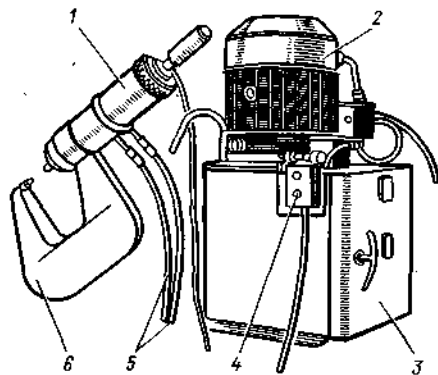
Установка для клепки рам: 1— силовая головка; 2— электродвигатель; 3— корпус; 4— пусковое устройство; 5— шланги; 6— скоба
